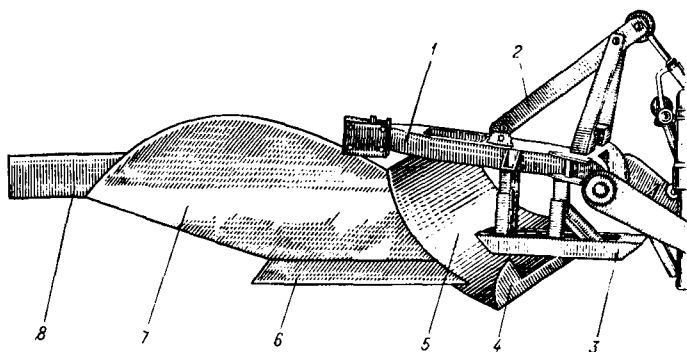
Плуг кустарниково-болотный навесной ПБН-100А:
